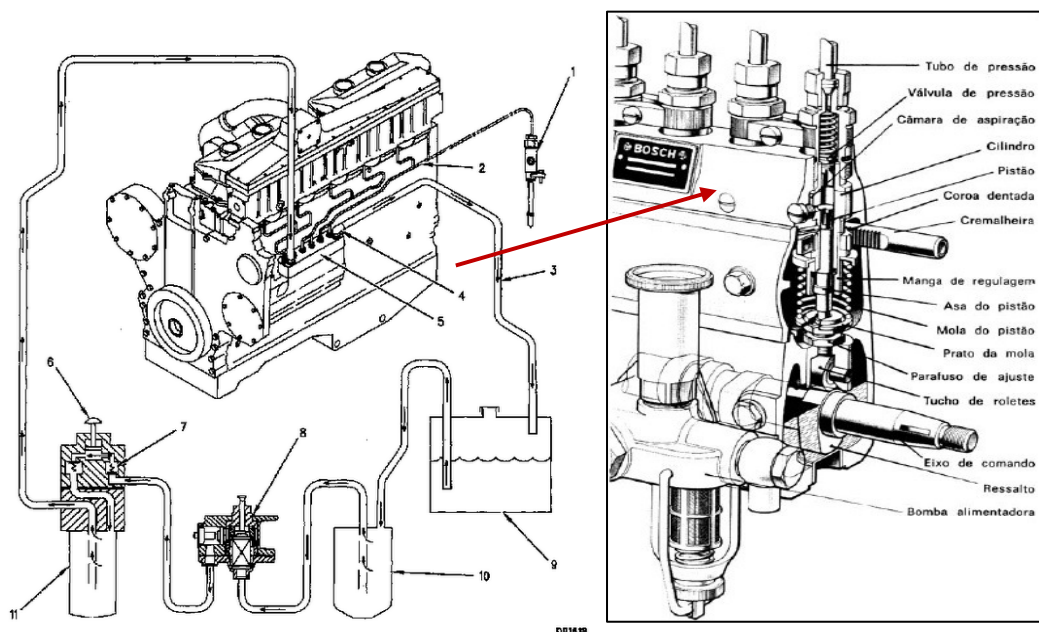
Esquema do sistema de combustível de um motor diesel e bomba de injeção de combustível da marca Bosch. (1)Bico de injeção de combustível; (2)Linhas de injeção de combustível; (3)Linha de retorno de combustível; (4) Orifício de sangria constante (parte do cotovelo), (5) Localização da bomba de injeção; (6) bomba de descompressão de combustível; (7) Válvulas de retenção; (8) Bomba de transferência de combustível; (9) Tanque de combustível; (10) Filtro de combustível primário; (11) Filtro de combustível secundário. Source: Marygar, 2013 & Santos, 2013.
